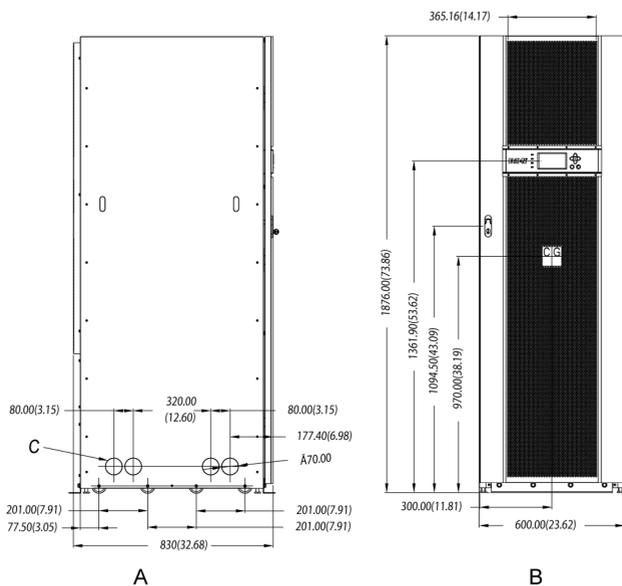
Габаритные размеры шкафа ИБП 93Е на 160-200 кВА (вид спереди и слева)
